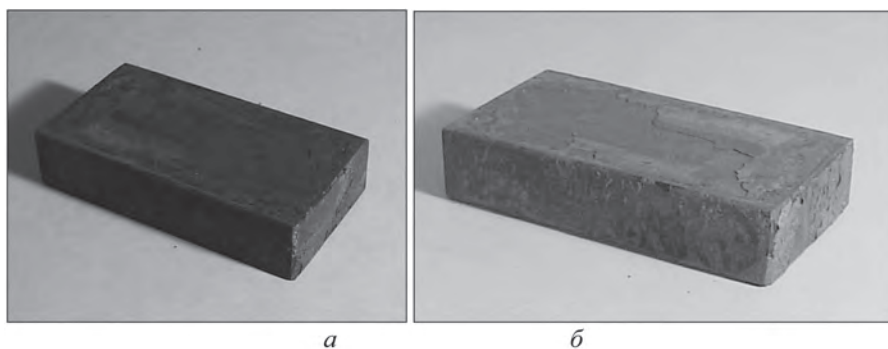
Модельный образец ножа ФТИ 5.001.1670 (77×44×15):
